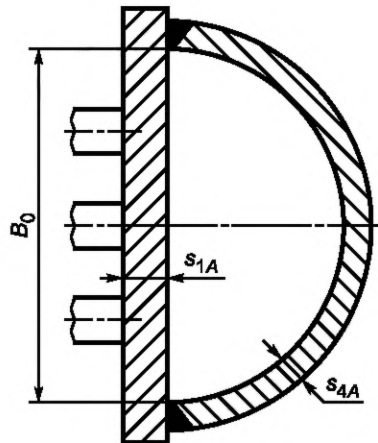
Камера неразъемной конструкции с полуцилиндрической задней стенкой
